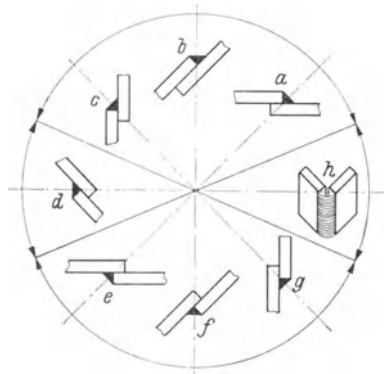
Lage des Arbeitsstückes bei verschiedenen Schweißarbeiten. *a, b, c* Waagrechtsschweißungen; *d* Senkrechtsschweißung; *e, f, g* Überkopfschweißungen; *h* stehende Senkrechtsschweißung.
